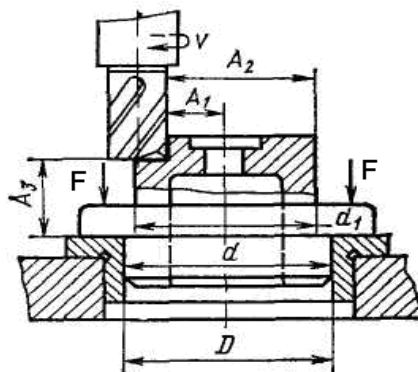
Схема установки заготовки при фрезеруванні (до задачі 1.25.)
